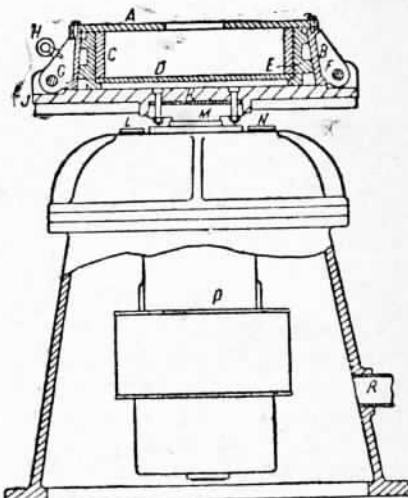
Внешний вид и разрез машины для отливки заготовок червячных шестерен.
